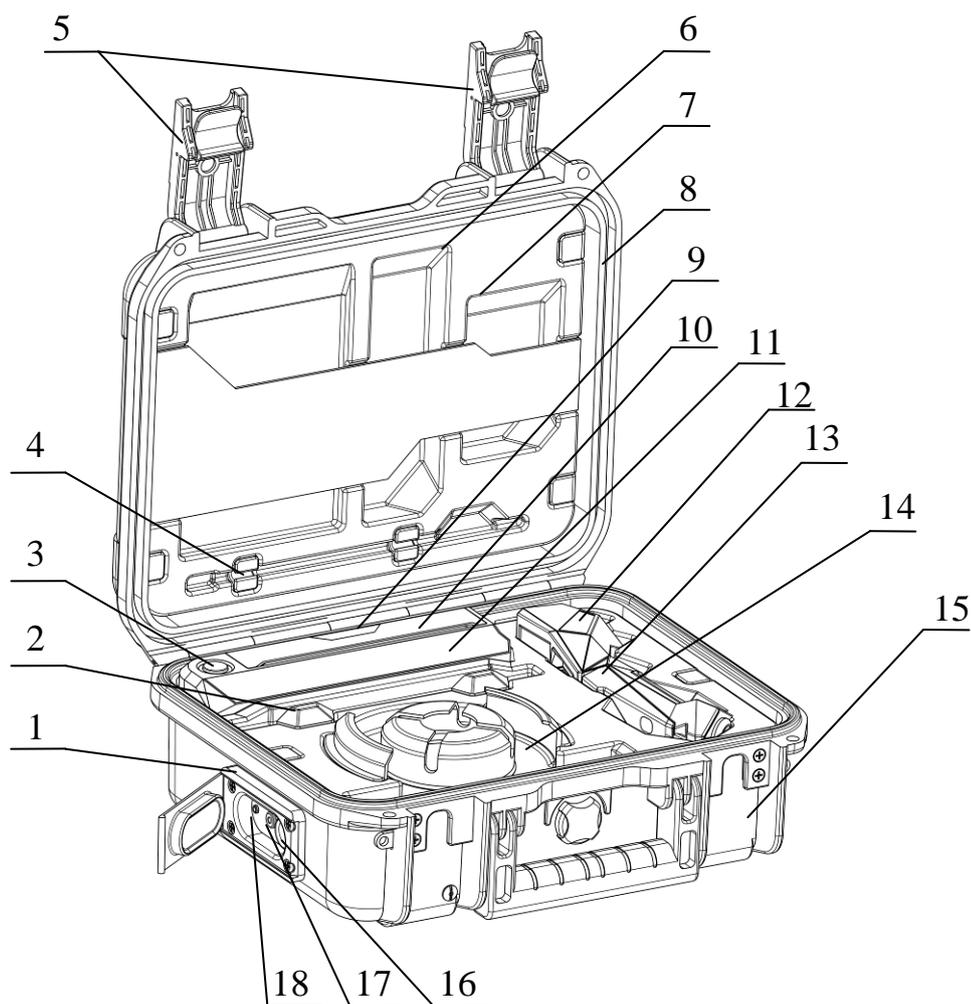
Внешний вид изделия, где: 1 — левая боковая крышка СТПР.010009.001 основного блока; 2 — посадочное место под гибкий пробоотборник; 3 — кнопка включения; 4 — посадочное место под телескопический пробоотборник; 5 — защёлки кейса; 6 — карман под сетевой шнур; 7 — карман под кабель USB A-B; 8 — верхняя крышка основного блока изделия; 9 — место маркировки изделия внутри основного блока; 10 — бардачок под аксессуары для проведения технического обслуживания; 11 — индикаторная панель; 12 — место маркировки пульта; 13 — пульт; 14 — посадочное место под основной кабель; 15 — кейс; 16 — разъём для подключения основного кабеля; 17 — разъём для подключения наушников; 18 — выпускной клапан.
